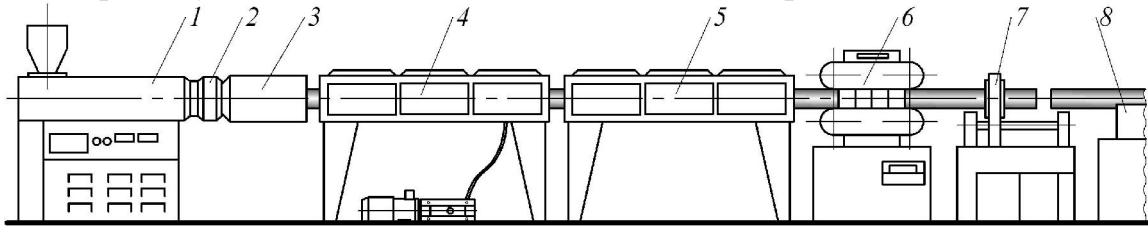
Принципова апаратно-технологічна схема виготовлення гладких полімерних труб: 1 – екструдер; 2 – трубна головка; 3 – калібрувальний пристрій; 4 – вакуум-ванна; 5 – ванна зрошення; 6 – тягнучий пристрій; 7 – відрізний пристрій; 8 – приймальний пристрій
